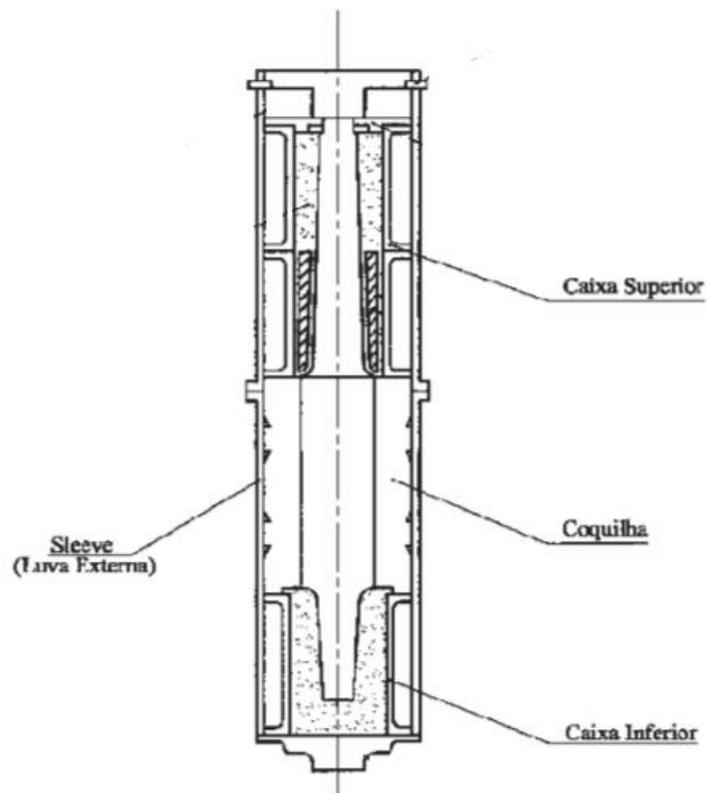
Esquema de conjunto montado para fundição na máquina centrífuga. (Fonte: Autor).
